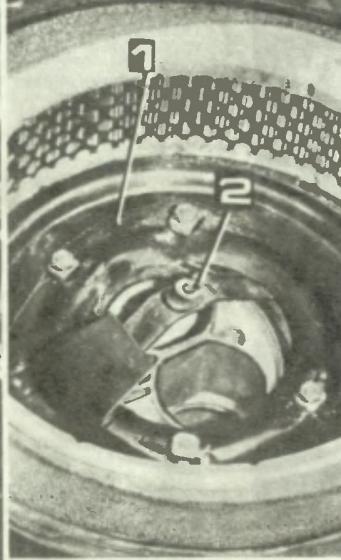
Корпус (1) фильтра, установленный на карбюраторе, и пластина (2) с гайкой для крепления крышки фильтра.
